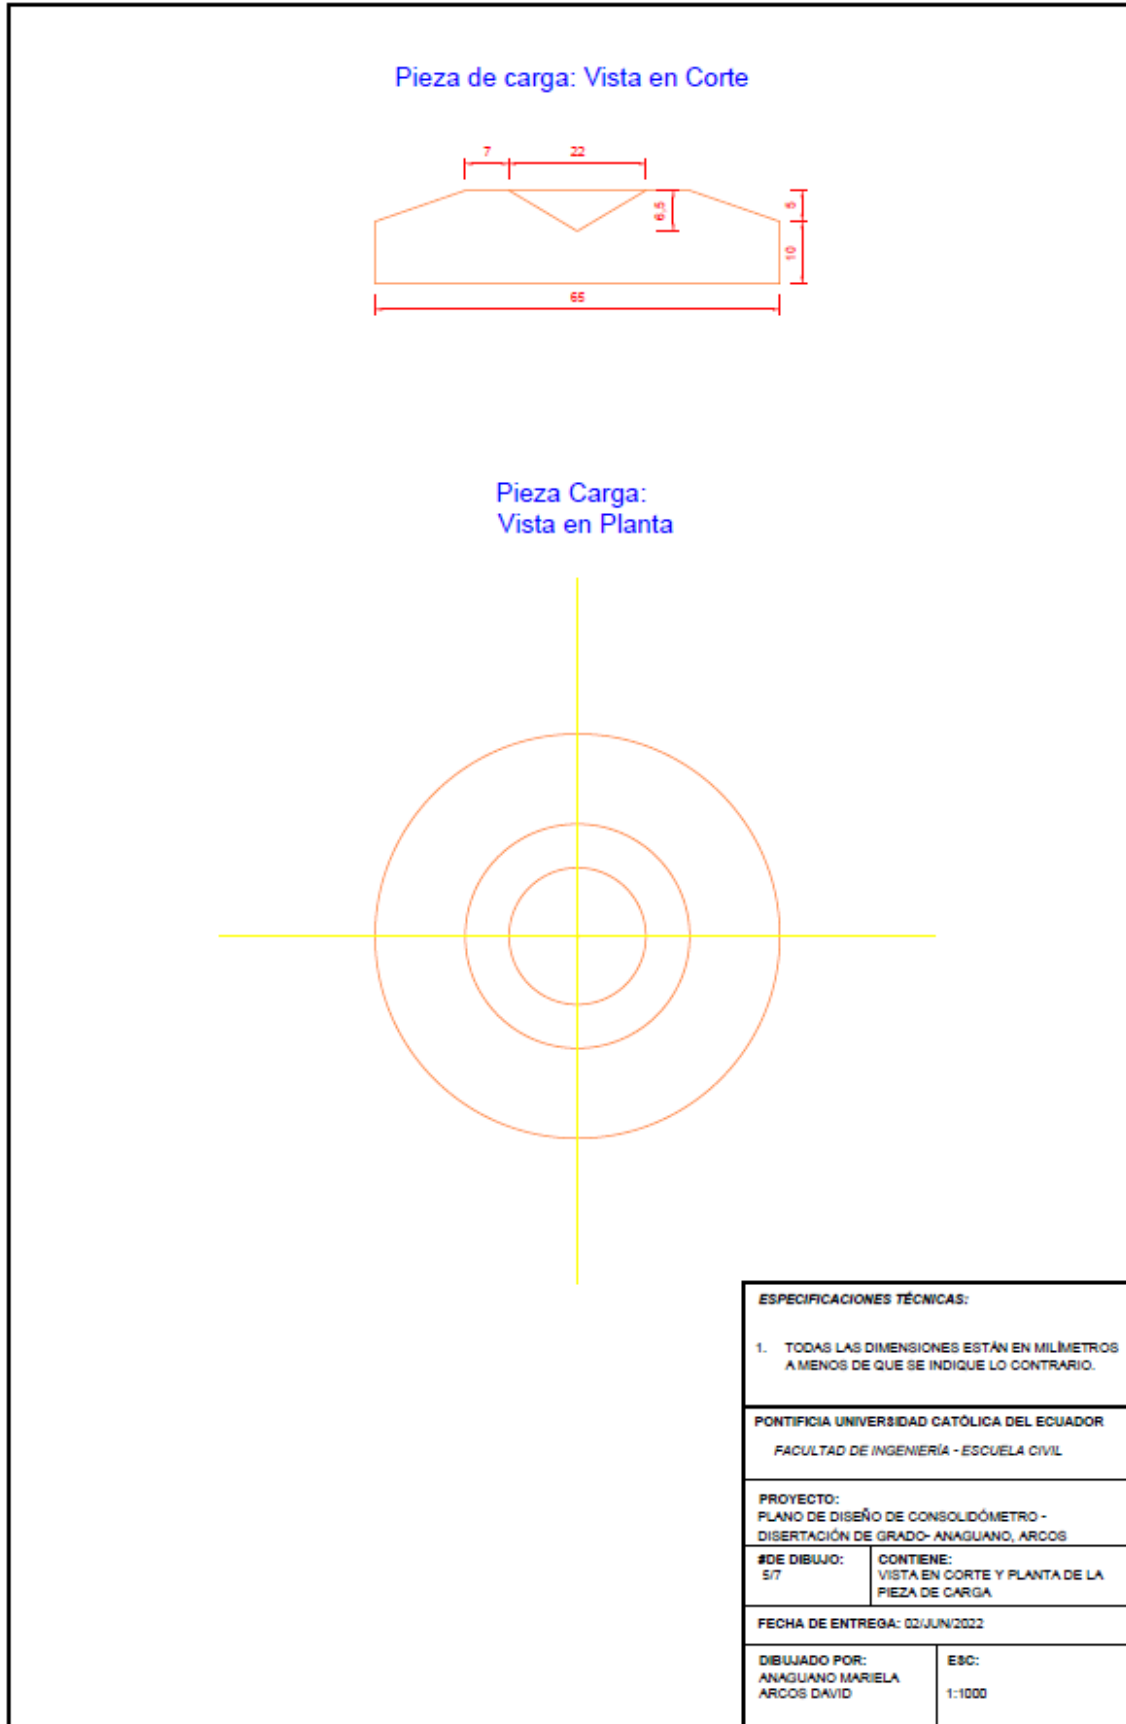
Plano de diseño del consolidómetro. Vista en corte y planta de la pieza de carga. Elaboración propia.
